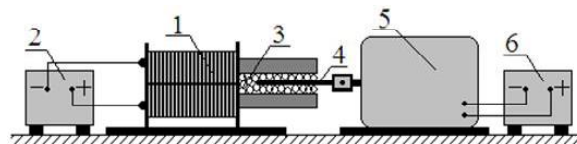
Схема установки для обработки лопаток стальными шариками в магнитном поле:
